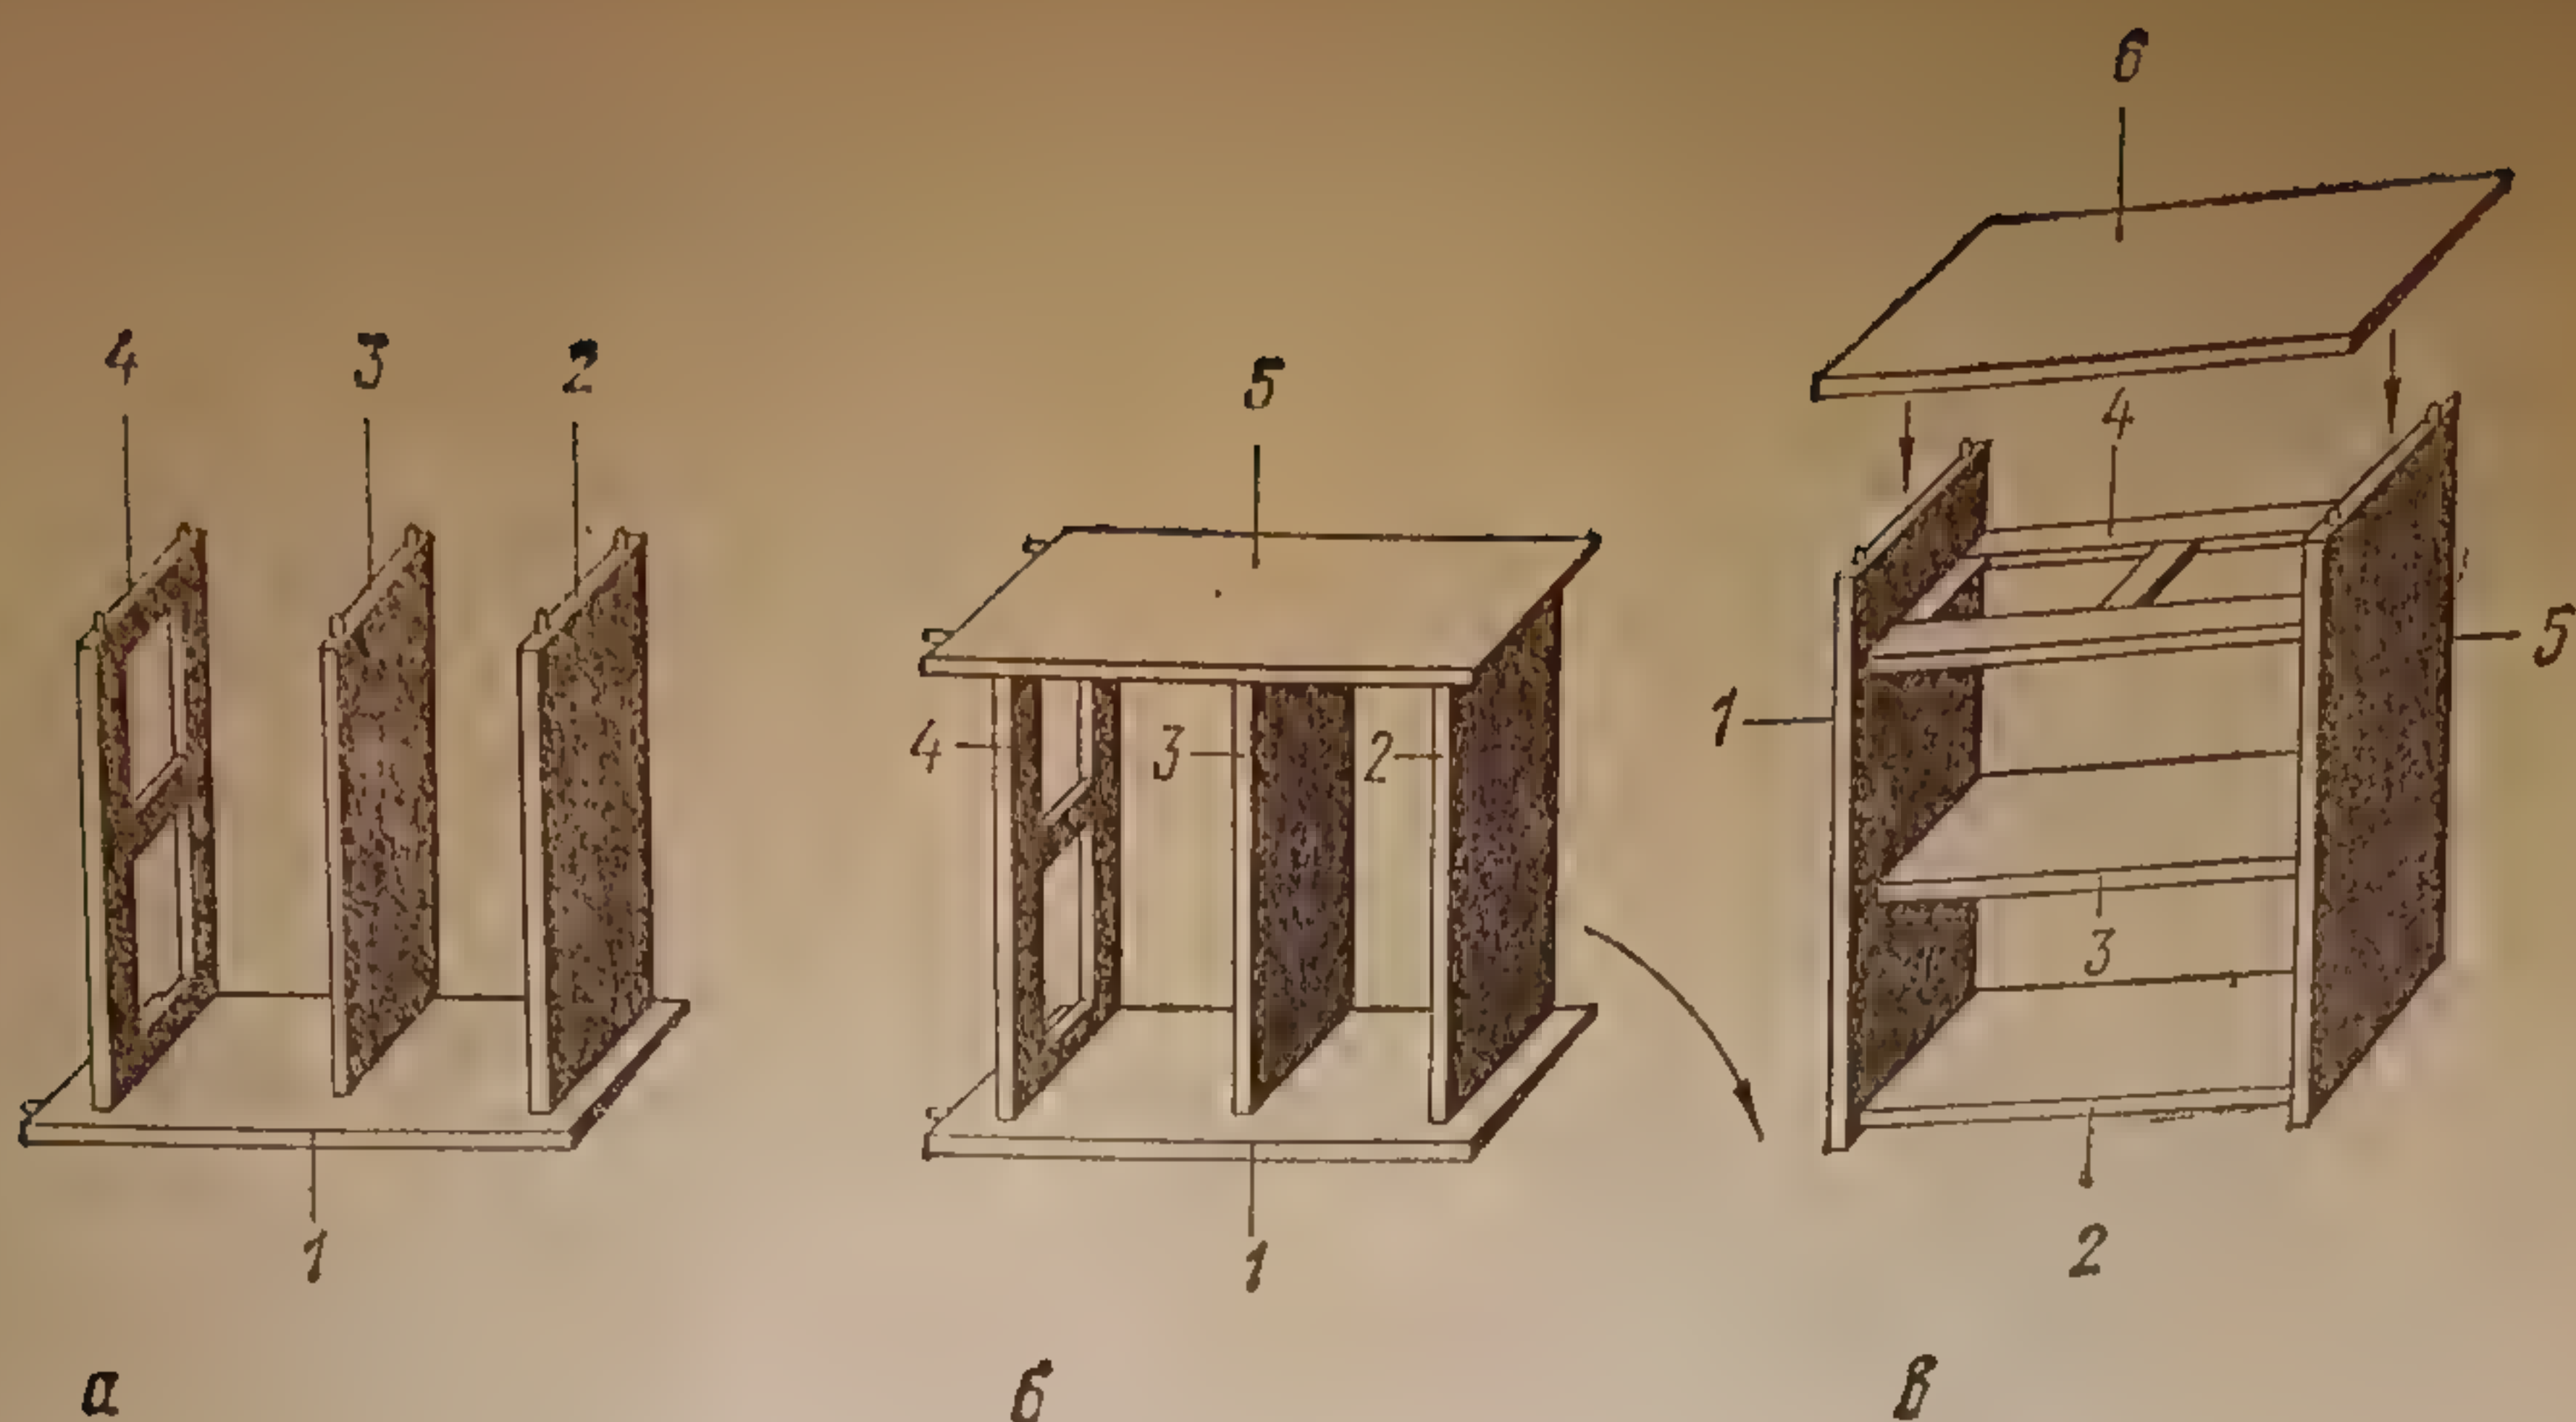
Сборка разделочного стола-шкафа: а — присоединение дна, полки и подъящичной рамки к боковой стенке; б — присоединение второй боковой стенки; в — присоединение крышки; 1 — первая боковая стенка; 2 — днище; 3 — полка; 4 — подъящичная рамка; 5 — вторая боковая стенка; 6 — крышка
